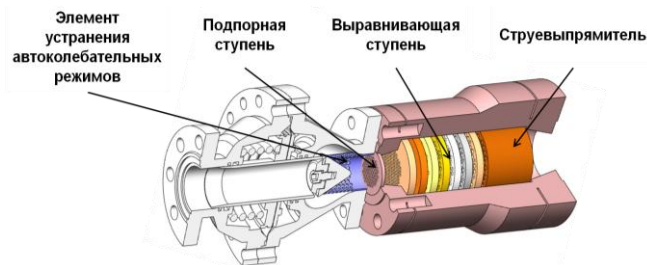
Внешний вид и конструктивная схема ГПД в сборе с регулятором
